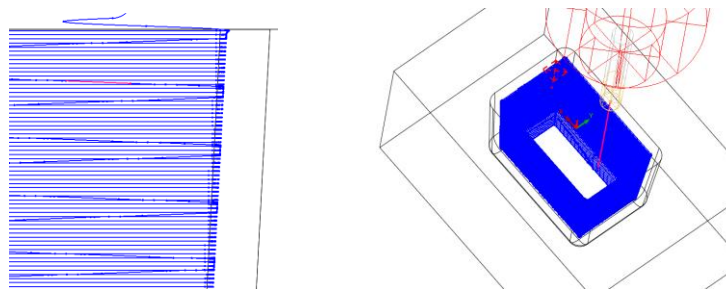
Траєкторія руху інструмента при напівчистовому фрезеруванні призматичного заглиблення
